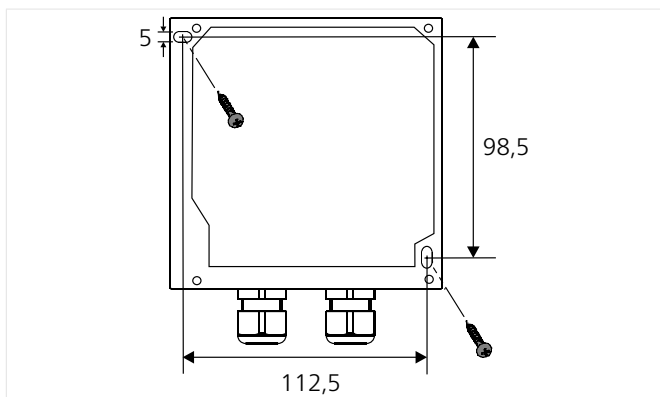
Abmessungen für Montagelöcher (Angaben in mm)
